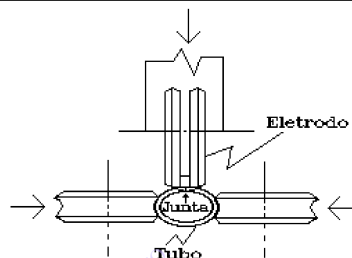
(d) - Soldagem de Tubos a Topo por Costura.
